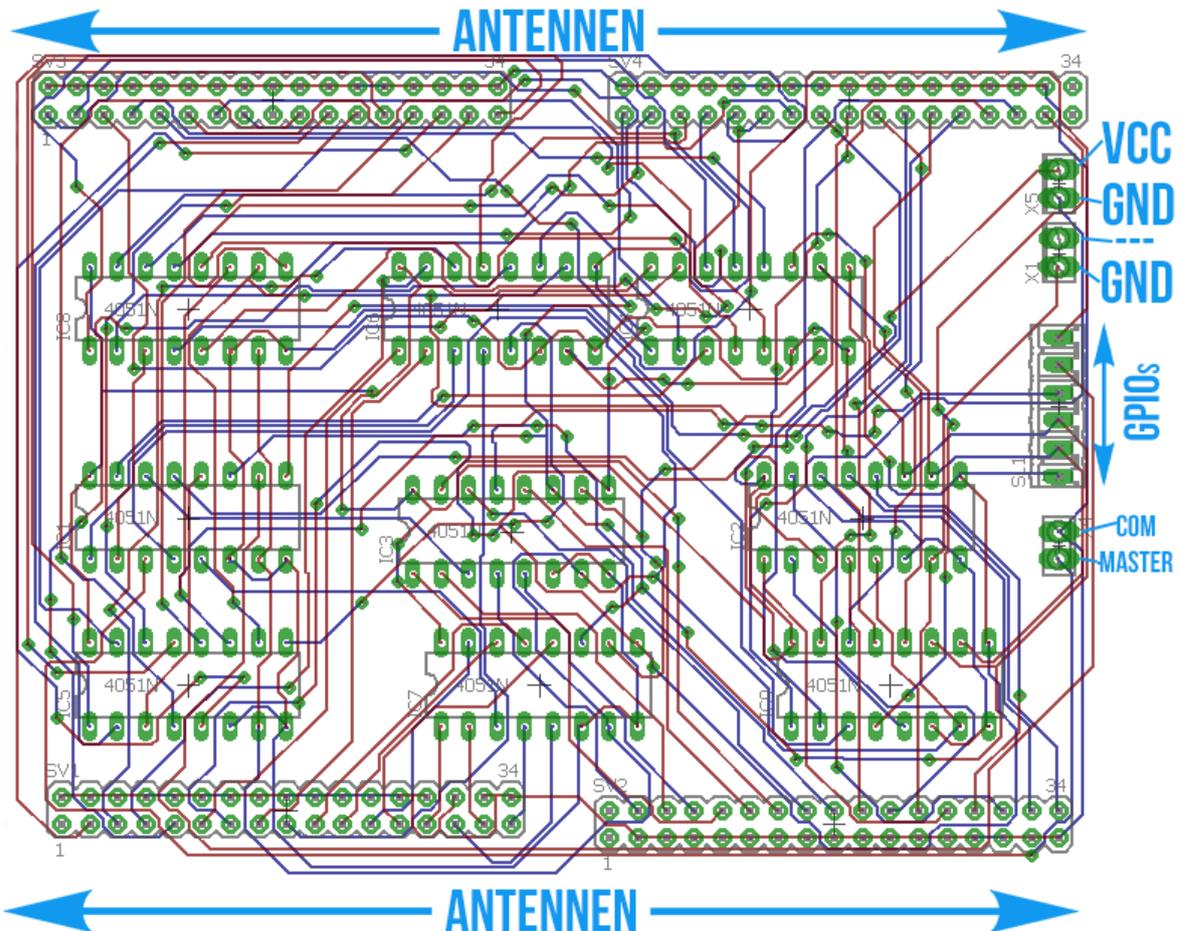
Zeigt die Anschlüsse des PCBs an
